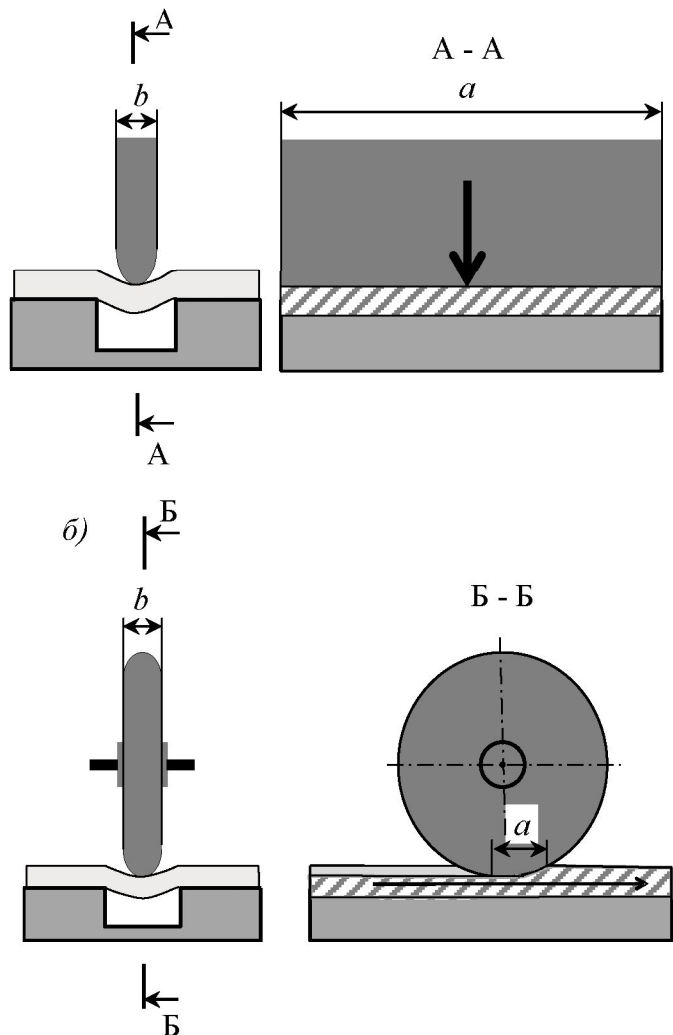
Схеми бігування з різними за формою бігувальними інструментами:
